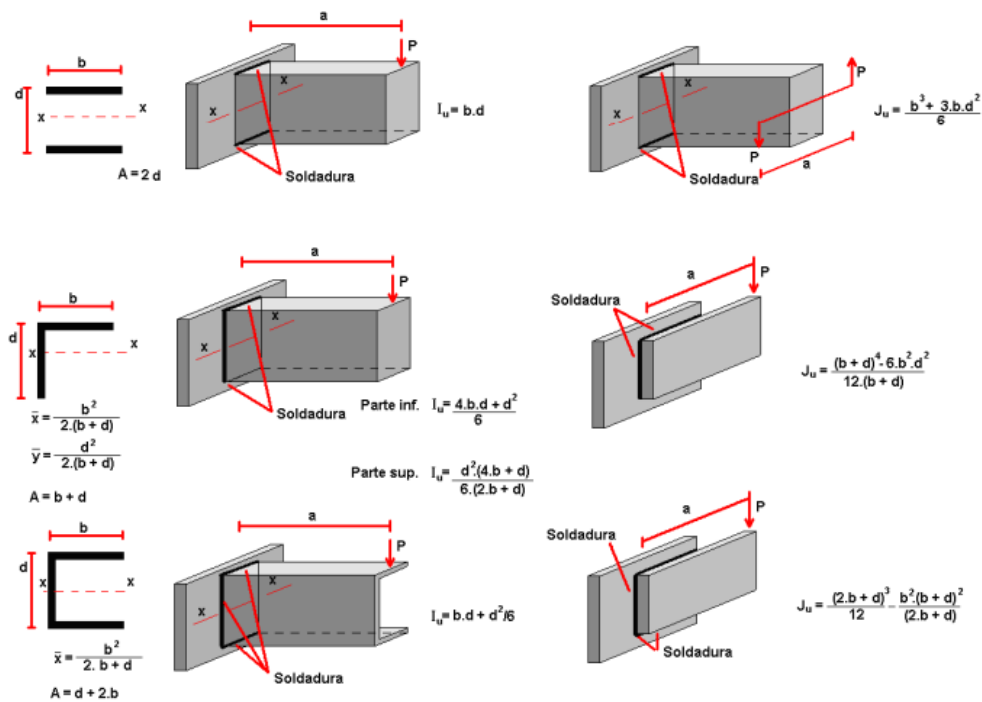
Tipos de soldadura y esfuerzos [24]
